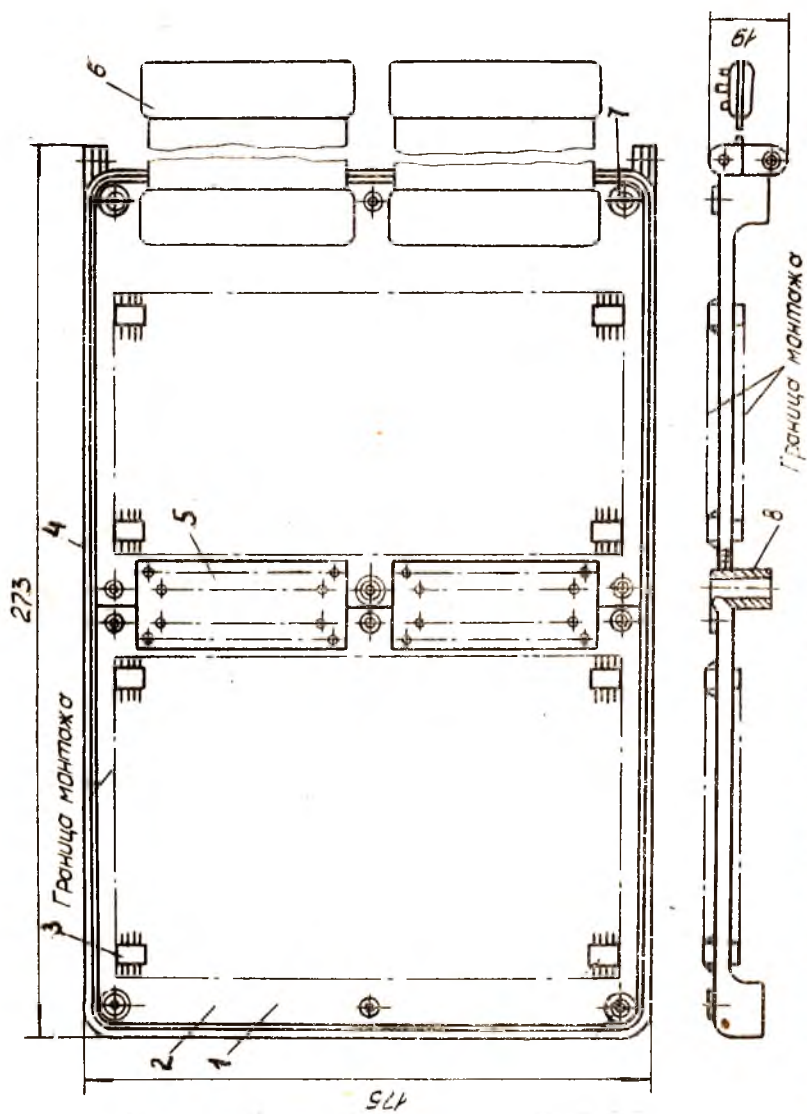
Двухслойная кассета блока книжной конструкции в рамочном исполнении; 1, 2 — печатные платы; 3 — микросхема; 4 — рама; 5 и 6 — гибкий печатный кабель; 7 — пустотелая закладка; 8 — втулка
